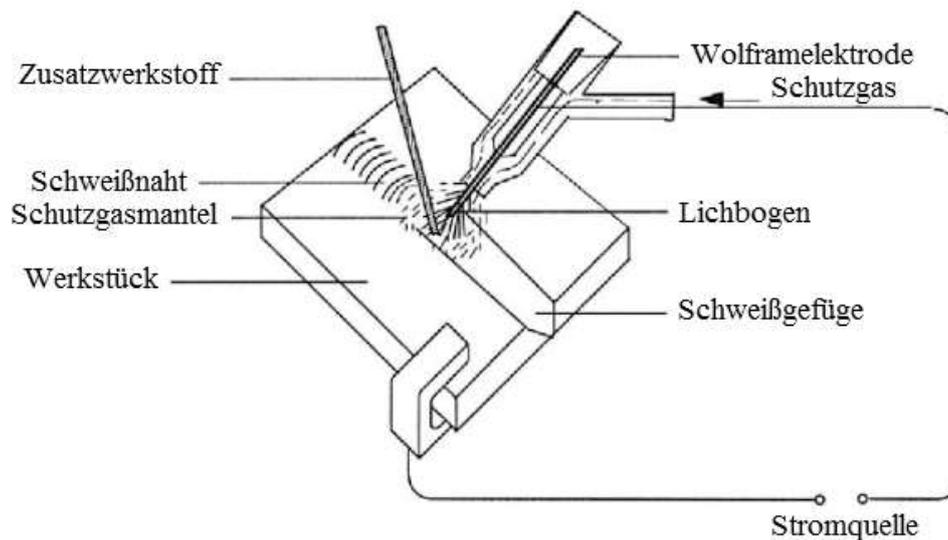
Verfahrensprinzip Wolfram - Inertgasschweißen (Quelle: /16,S.79/)
